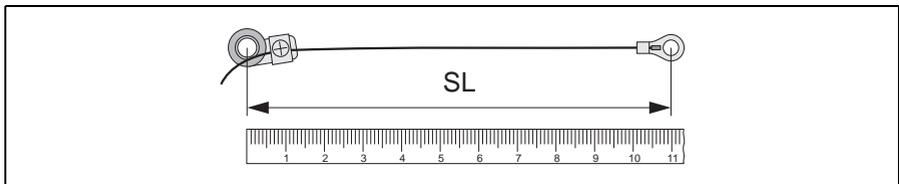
Fixierteil (a) und Kabelschuhe (b) mit einem Abstand entsprechend der Schnurlänge (SL)
